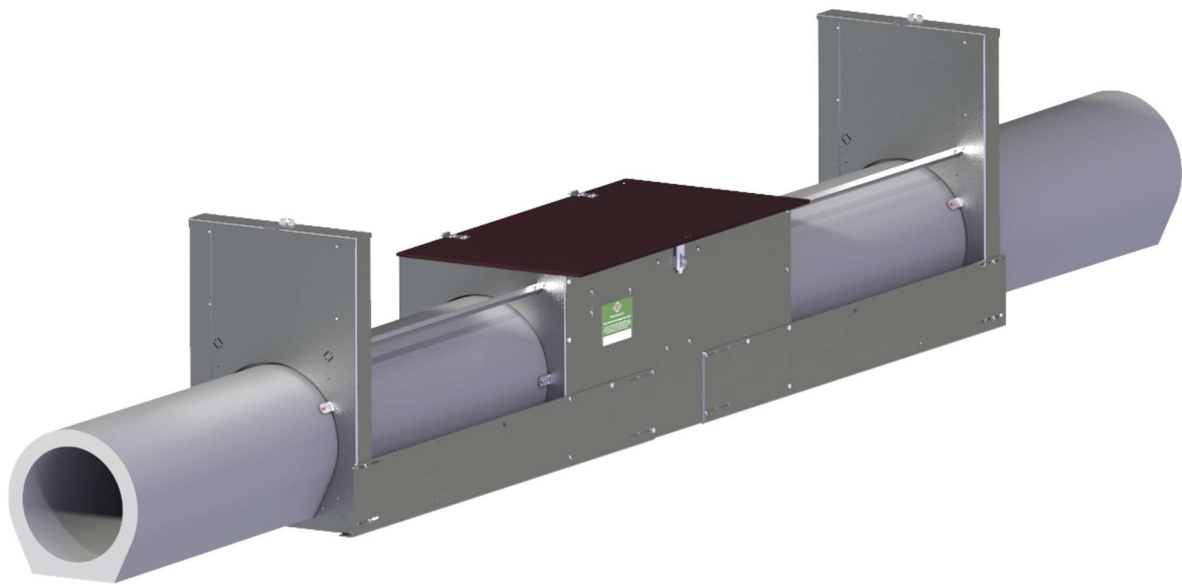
Falle mit montierten Hauptkasten- und Schieberkastendeckeln
